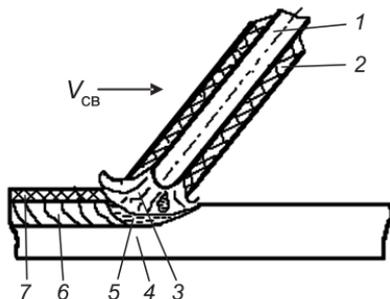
Схема процесса ручной дуговой сварки (ММА)
